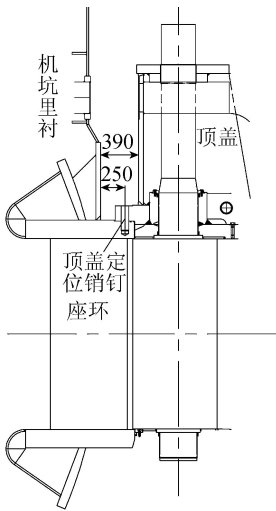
顶盖定位销钉孔施工位置示意图(单位:mm)
